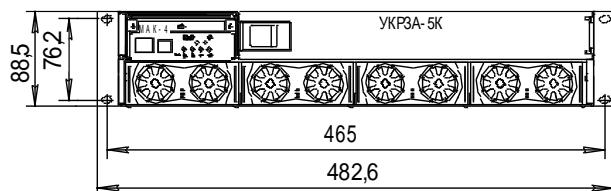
Габаритный чертеж УКРЗА-5К
